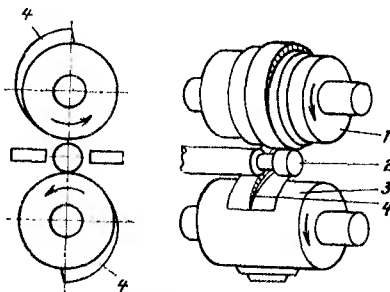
Схема поперечно-клиновой прокатки заготовок круглыми роликами
